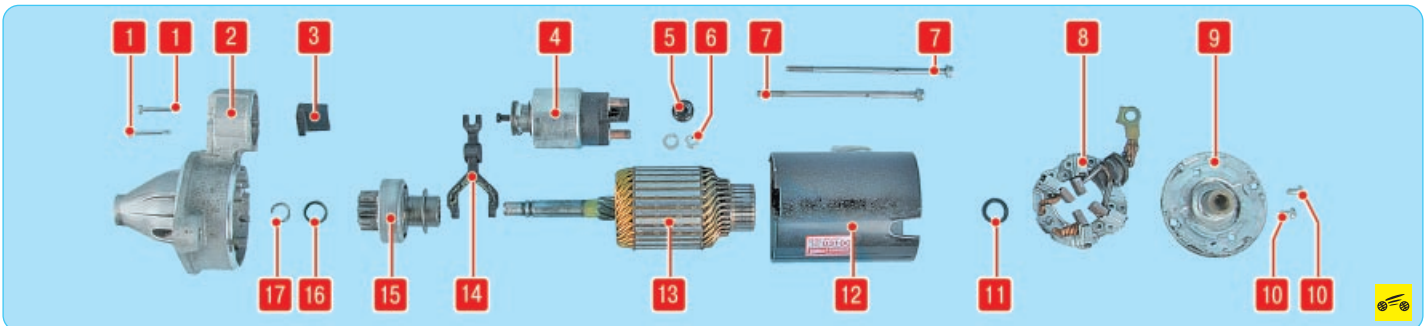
Детали стартера: 1 – винт крепления тягового реле; 2 – передняя крышка; 3 – опора рычага привода муфты свободного хода; 4 – тяговое реле; 5 – гайка контактного болта; 6 – гайка с шайбой крепления силовой шины; 7 – стяжной болт; 8 – щеточный узел; 9 – задняя крышка; 10 – винт крепления щеточного узла; 11 – дистанционное кольцо; 12 – корпус статора; 13 – ротор; 14 – рычаг привода муфты свободного хода; 15 – муфта свободного хода; 16 – ограничительное кольцо муфты свободного хода; 17 – стопорное кольцо
